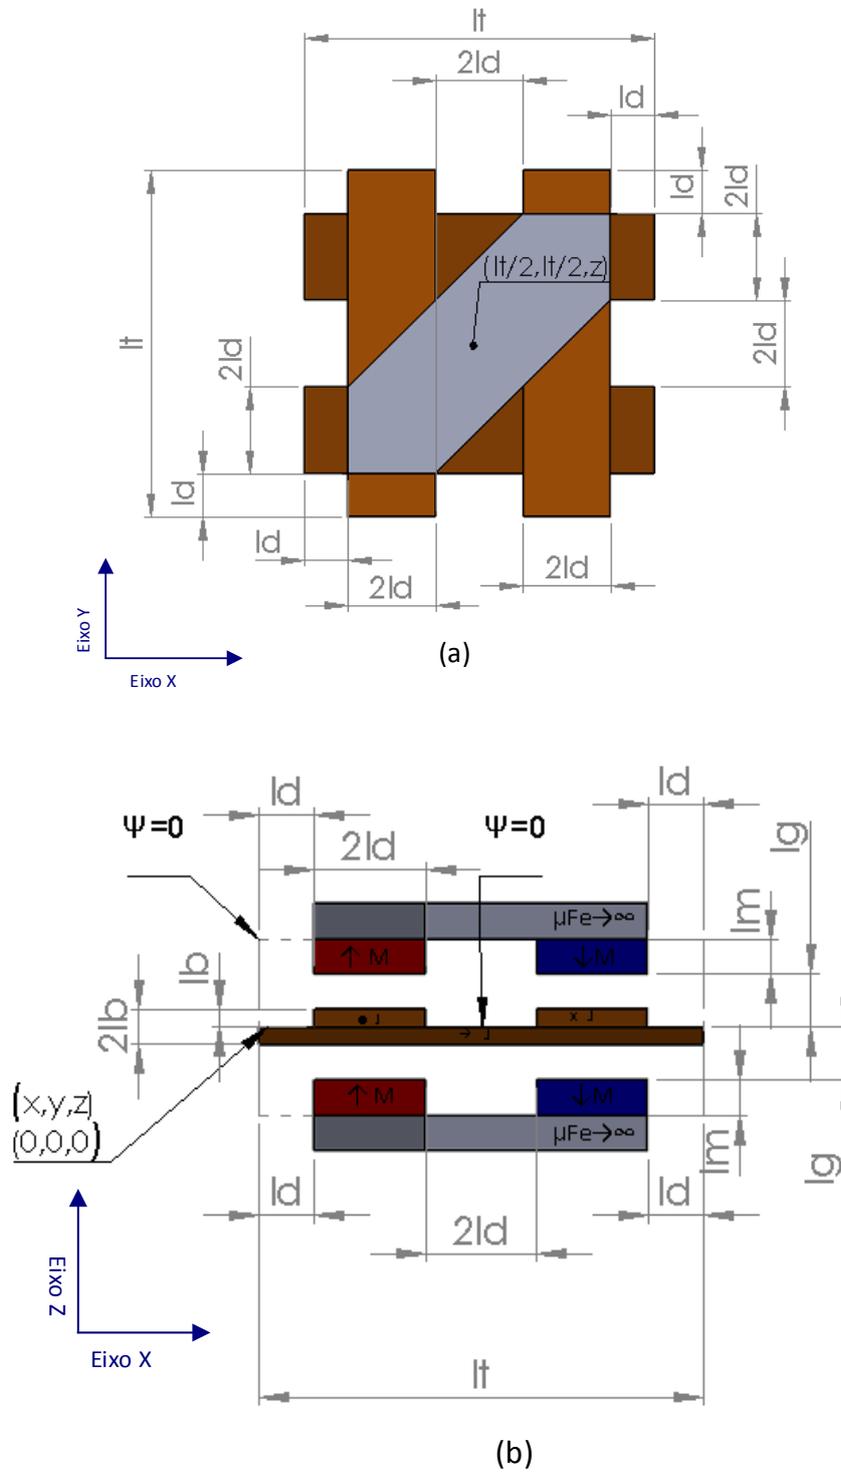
Desenho da geometria do atuador planar: (a) vista superior e (b) vista frontal.
